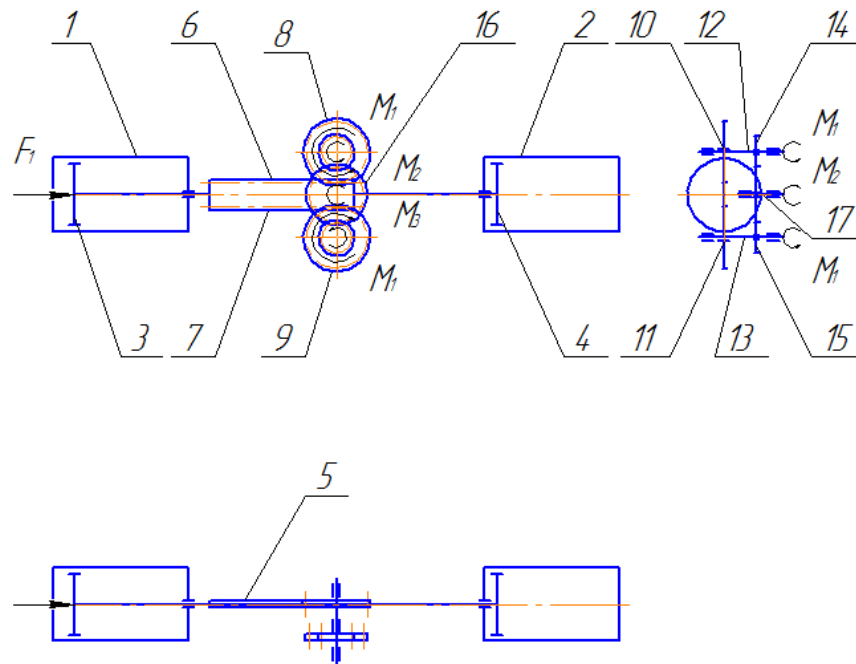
Схема двотактного поршневого опозитного двигуна при робочому ході першого циліндра: 1, 2 – циліндри; 3,4 – поршні; 5 - зубчаста рейка; 6, 7 – зубці; 8, 9 – шестерні; 10, 11 - обгінній муфті; 12, 13 - вали; 14, 15 - додаткові шестерні; 16 - центральне зубчасте колесо; 17 - вал
